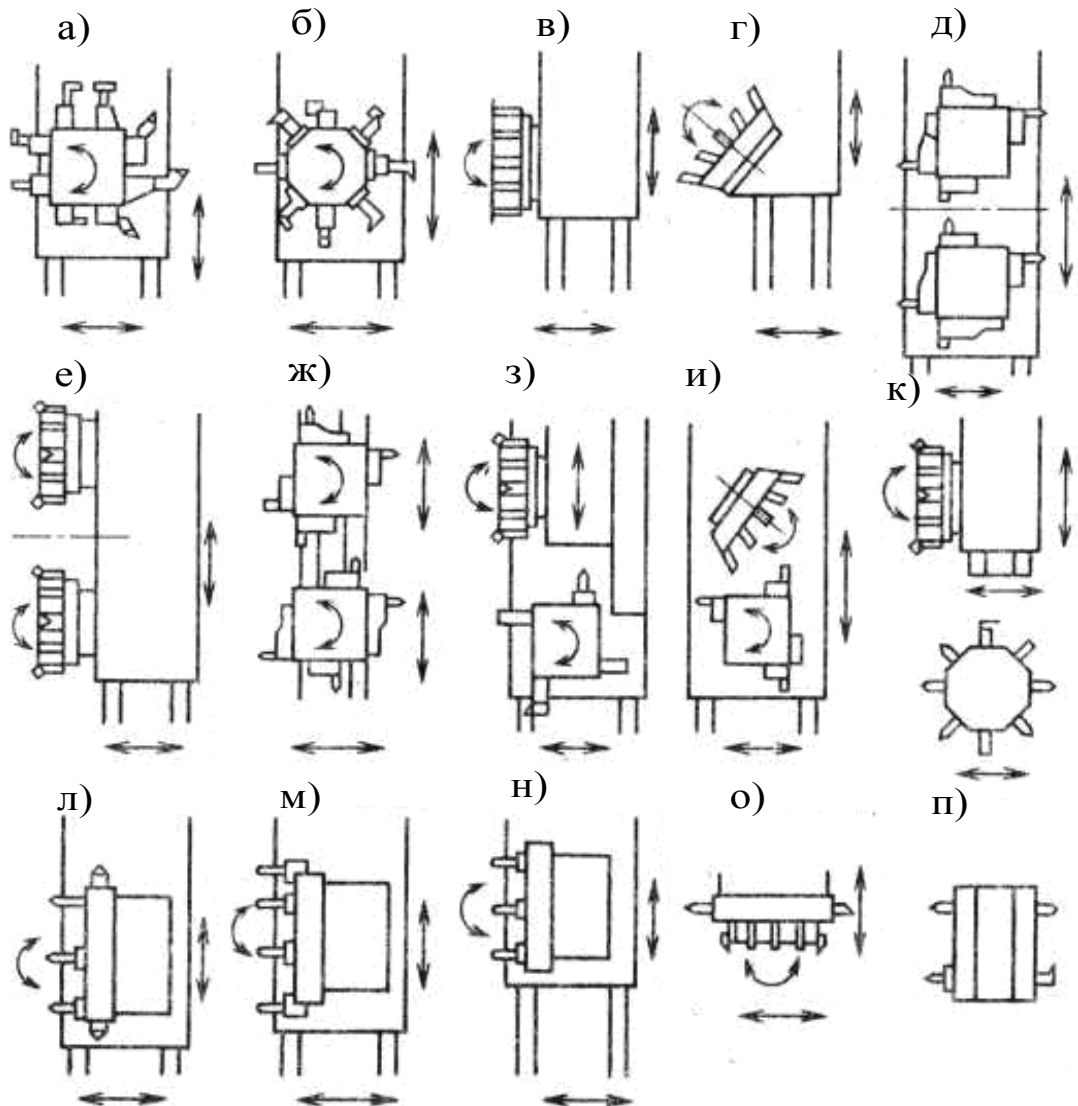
Схемы конструктивного исполнения револьверных головок токарных станков
